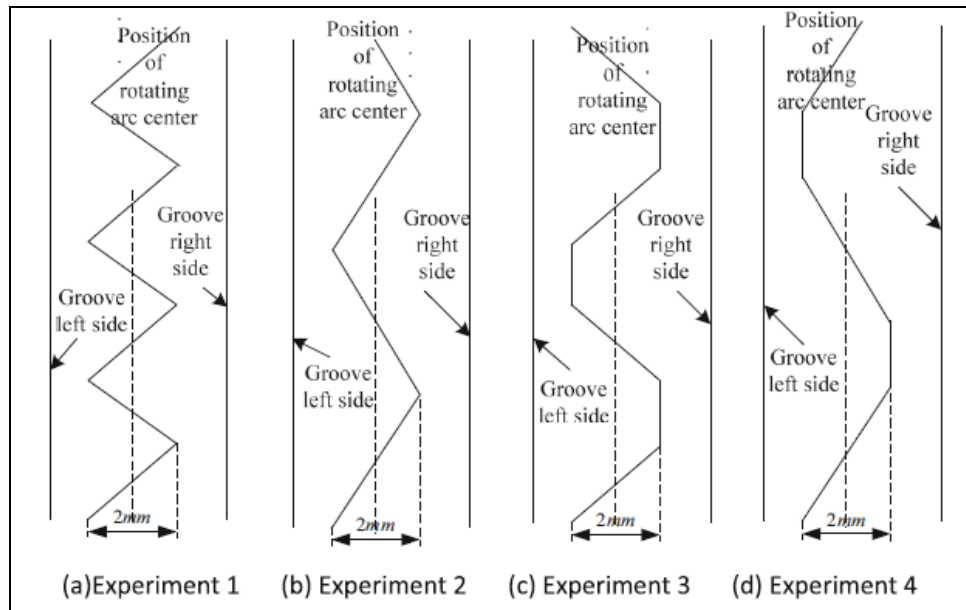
Oscilação lateral para soldagem com eletrodo rotativo [19]
